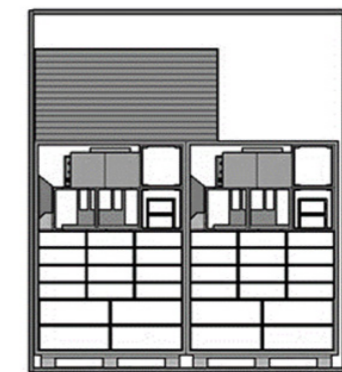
Embalaje de dos estructuras en caja de madera sobre palet europeo
